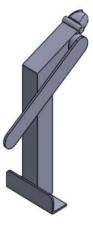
CAD del dispositivo que ayuda a remover la semilla del durazno de forma manual. (Fuente: Autor).
